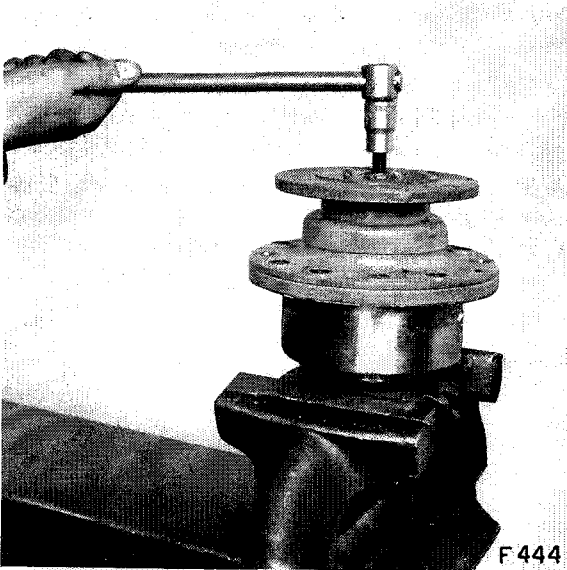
Lösen der Inbusschrauben im Flanschzentrum
